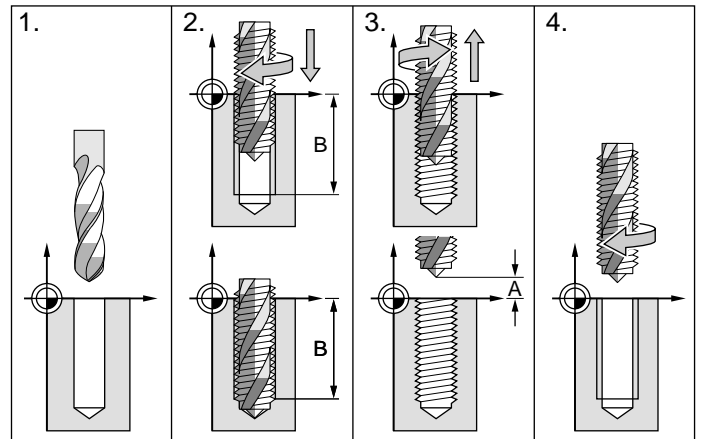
Zyklus-Ablauf Gewindebohren
